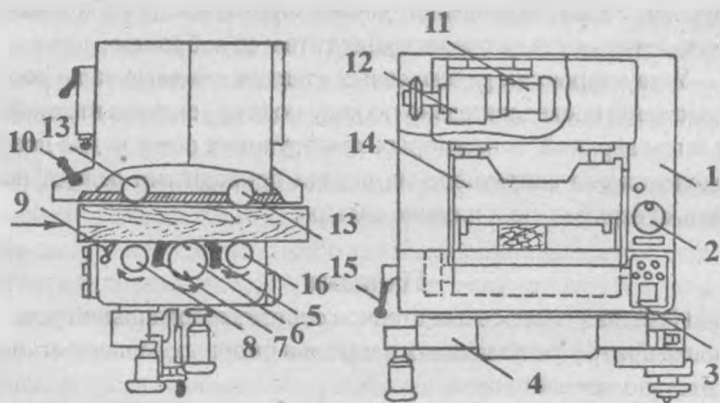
Односторонний рейсмусовый станок СР6-9:
